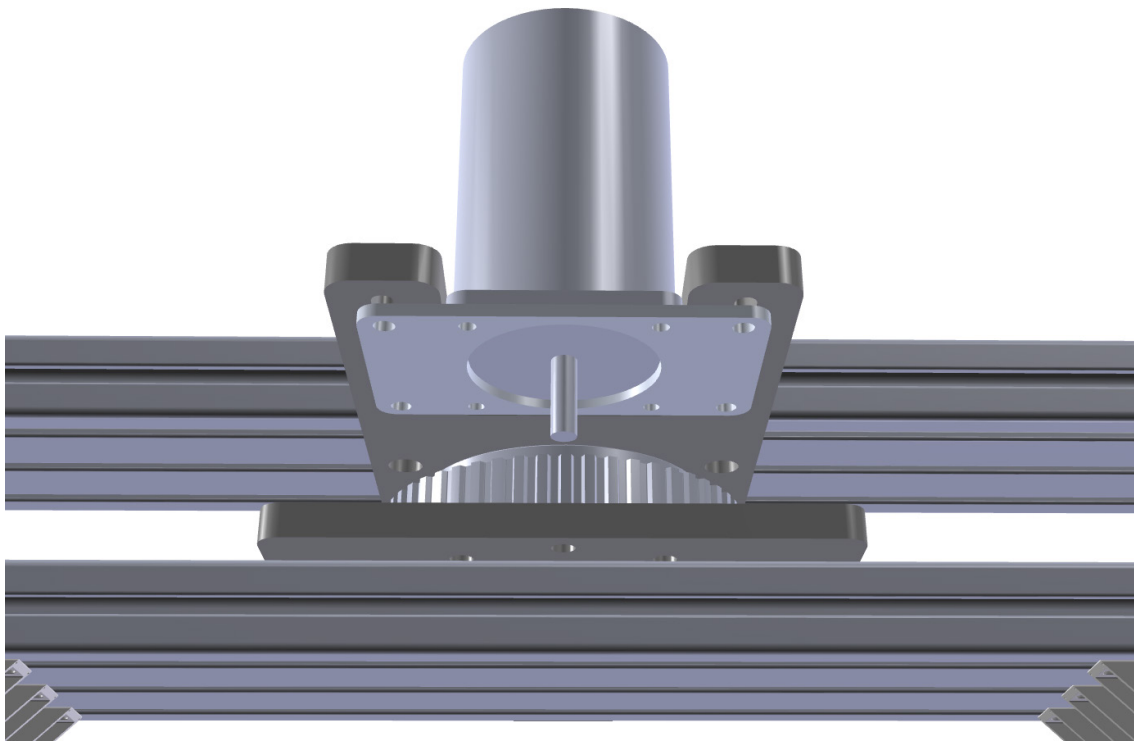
Detailansicht der Schwenkachse II mit Rundtischlager, Schrittmotor, Flanschadapter und Zahnriemenvorspanneinheit.
